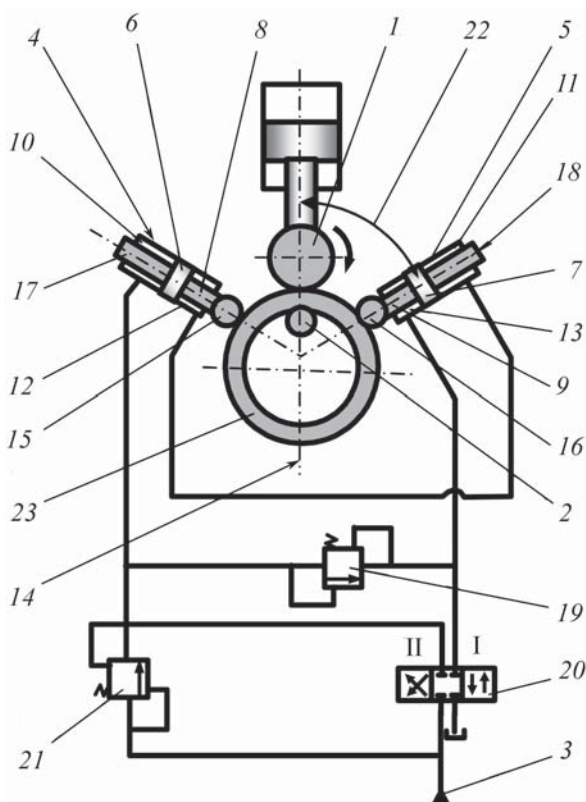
Гидромеханическая схема машины для раскатки кольцевых заготовок (патент РФ № 2243054)
